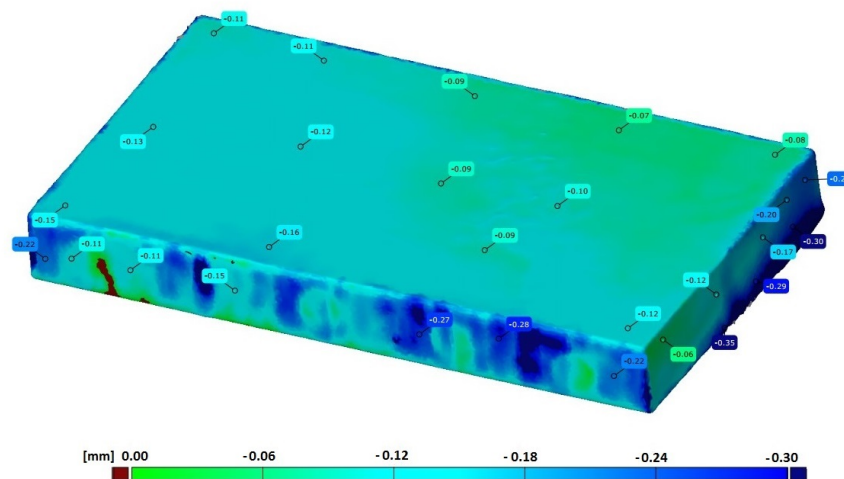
Controlo dimensional da chapa de Ti-6Al-4V
